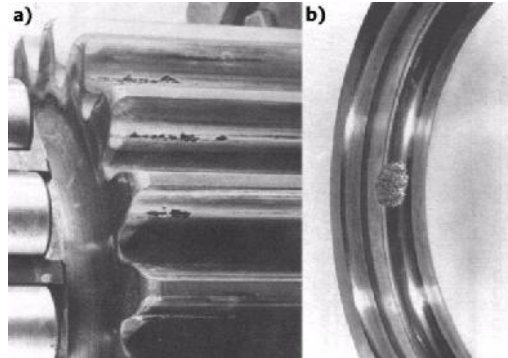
Aspecto de superficies sometidas a fatiga de contacto. a) flanco activo de un diente de engranaje, b) pista de un rodamiento.
